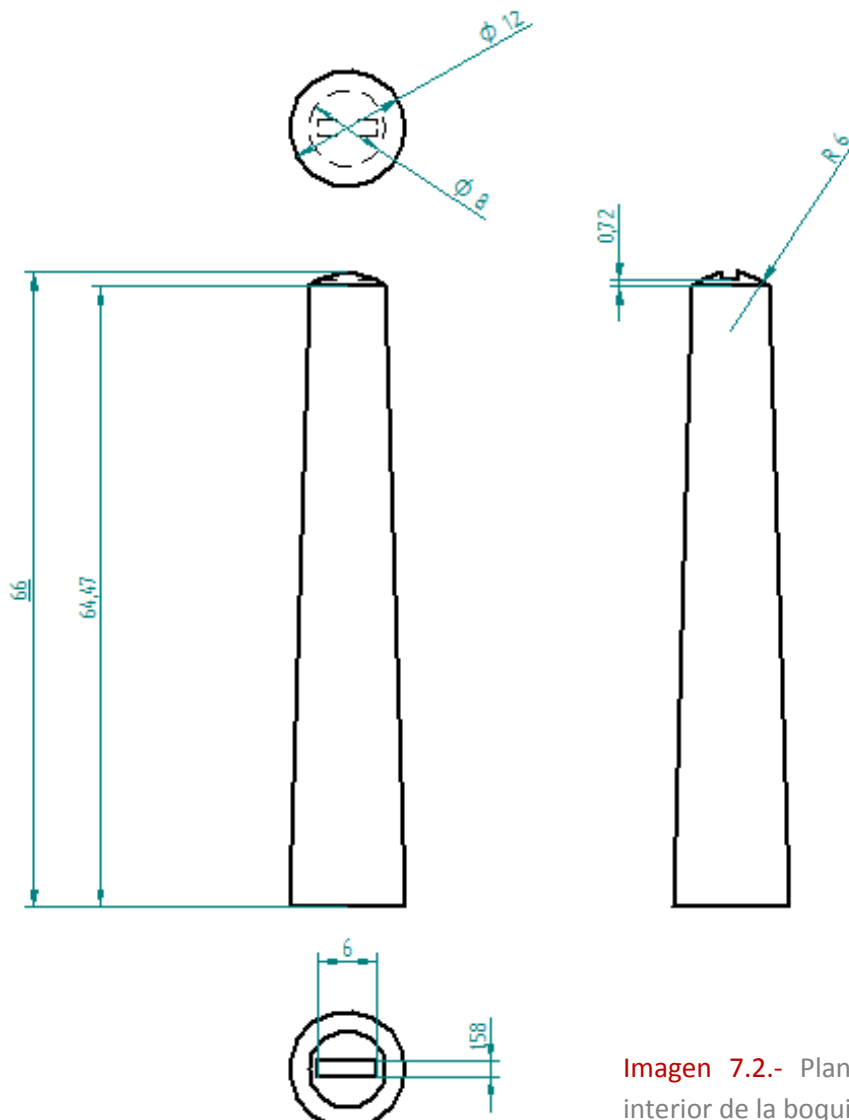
Planos de la zona interior de la boquilla propuesta
